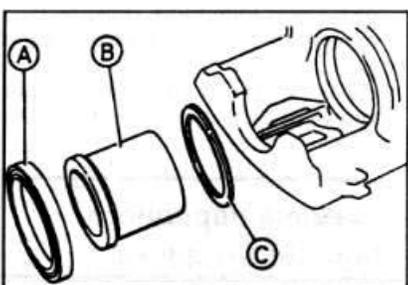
Детали суппорта переднего тормоза Bendix. А - пылезащитный чехол. В - поршень. С - уплотнительное кольцо поршня.
